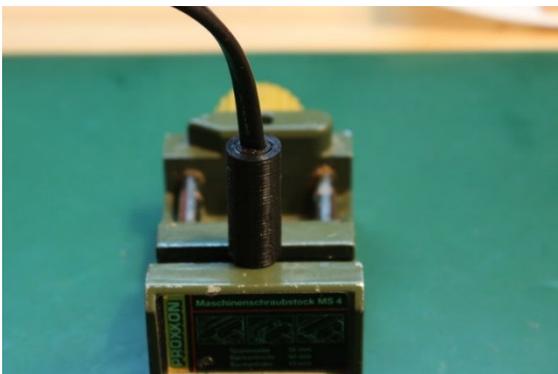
Einkleben der Steckerabdeckung/Kabeldurchführung
